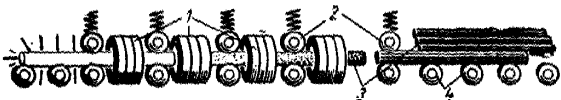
Схема нагревателя с секционированным индуктором и роликовым механизмом для транспортирования заготовок:
